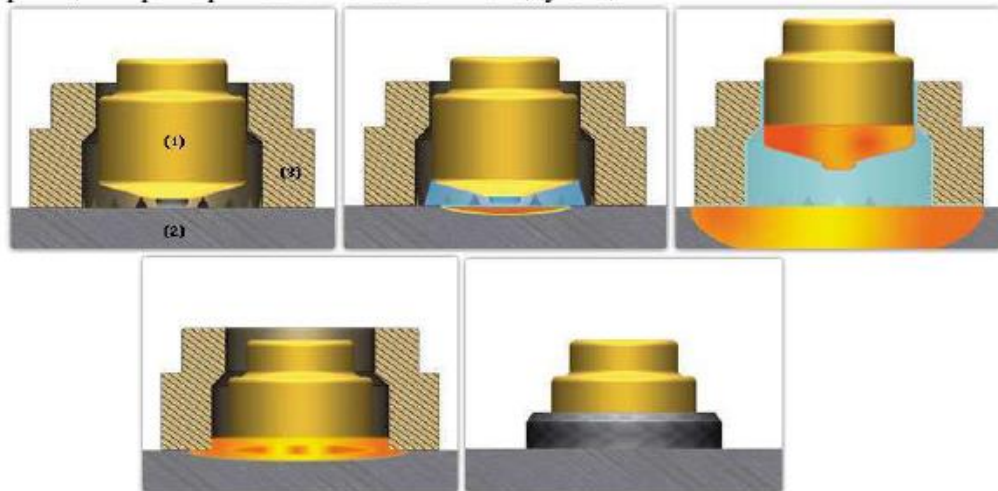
Принцип приварки твердосплавных шипов TungStud.
